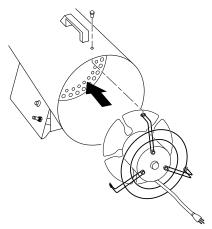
Remise en place du moteur et de la grille du ventilateur
